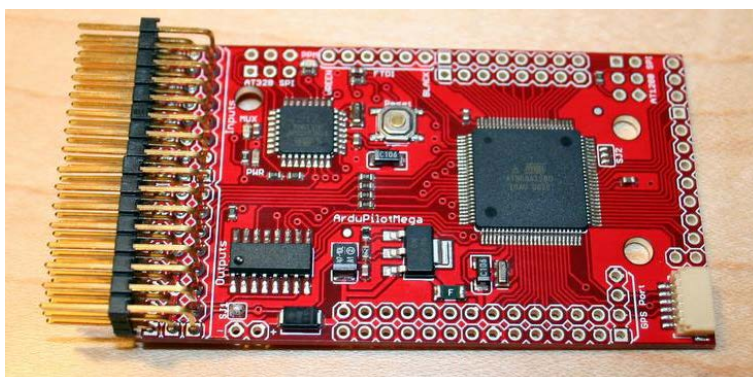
Placa APM com os *headers* de 90° soldados [42]
